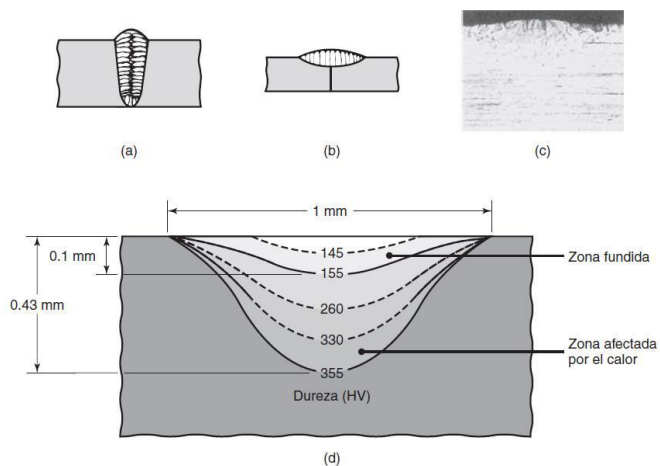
Estructura de los granos en una unión de soldadura.
